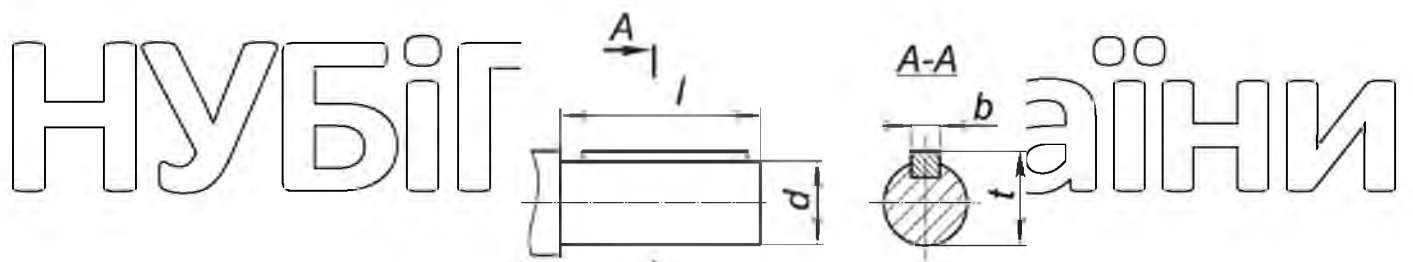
Приєднувальні параметри циліндричних валів мотор-редукторів ЗМП планетарного виконання [26]
